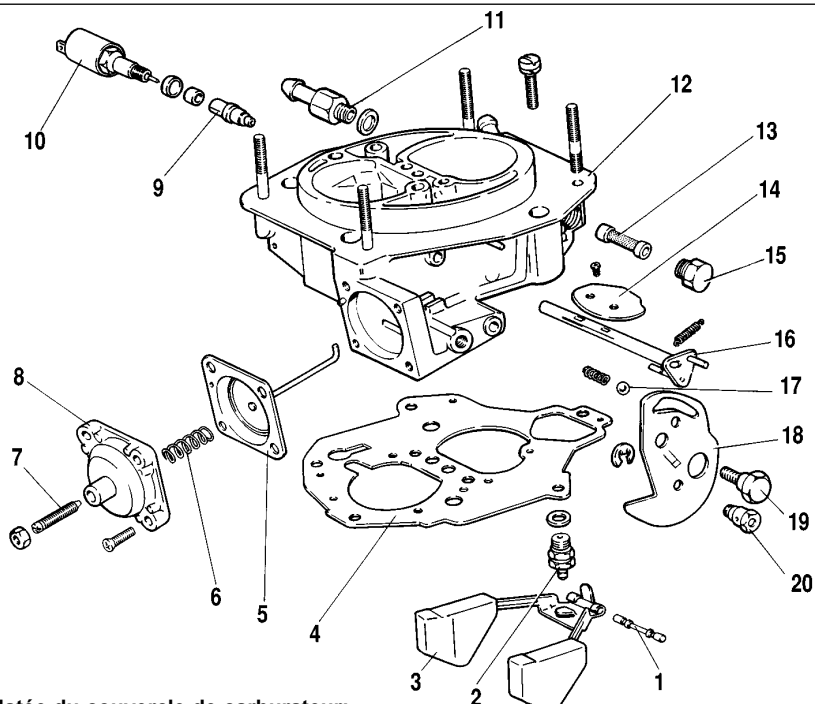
Vue éclatée du couvercle de carburateur:
